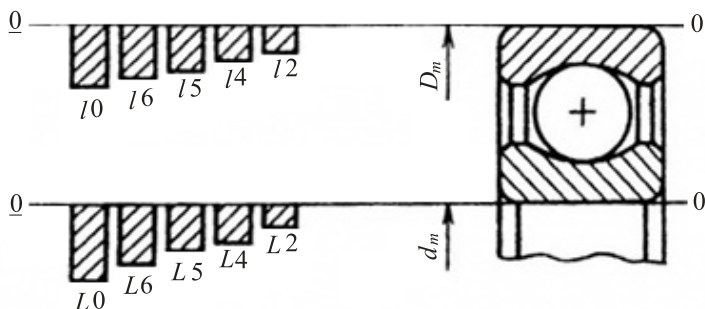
Схема расположения полей допусков для подшипников
